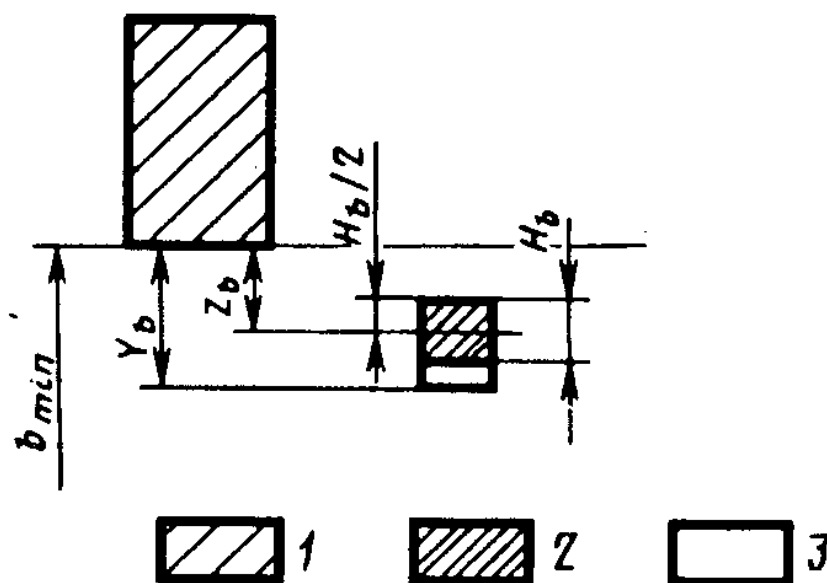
Расположение поля допуска размера b_k калибр-пробки:
